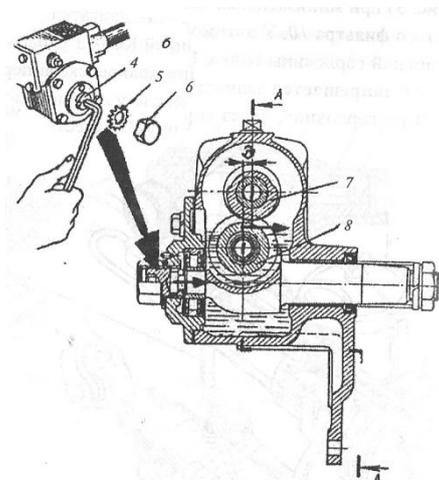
Регулировка рулевого механизма ГАЗ-53А:
